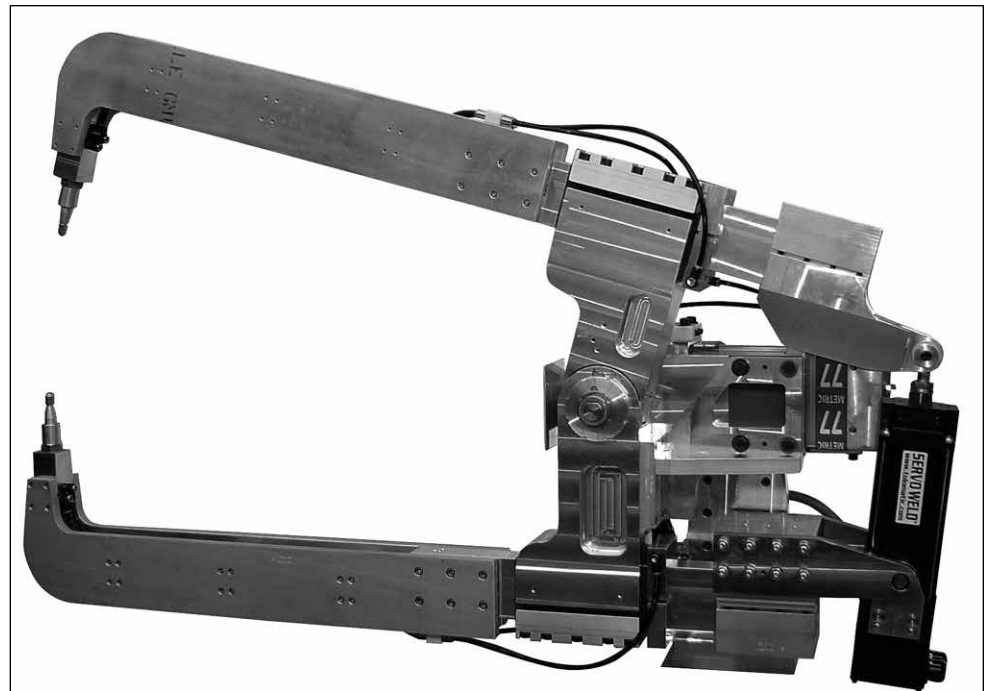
Exemplo de acionador de solda (GSWA04) instalado em uma unidade de pistola de solda estilo "X".
